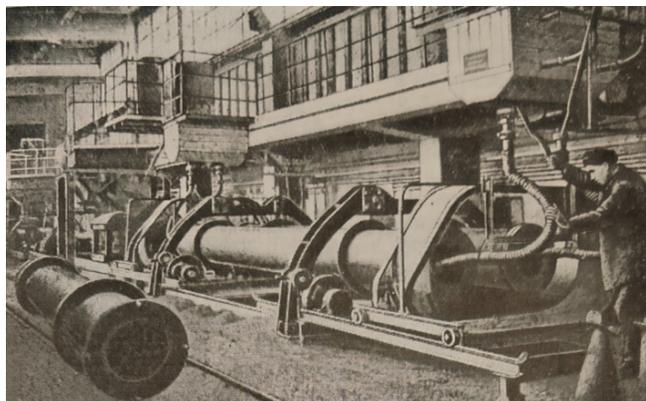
Центробежный станок для изготовления железобетонных водопроводных труб
